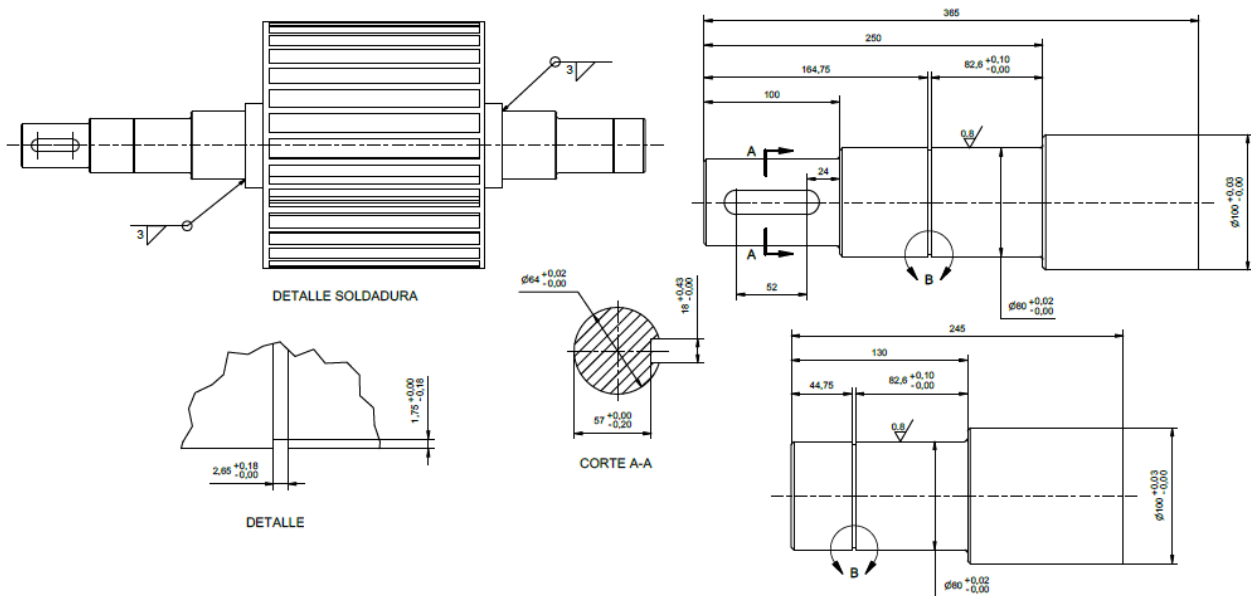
Plano de ensamble soldado: Rotor. Detalle de semiejes.
